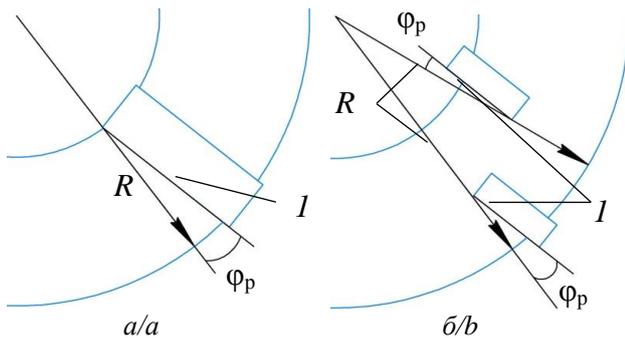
Схема изменения фронтального угла резца PDC (вид с торца коронки): а) один резец; б) несколько резцов в матрице; 1 – режущая грань PDC; φ_p – фронтальный угол установки резца; R – наружный радиус буровой коронки
